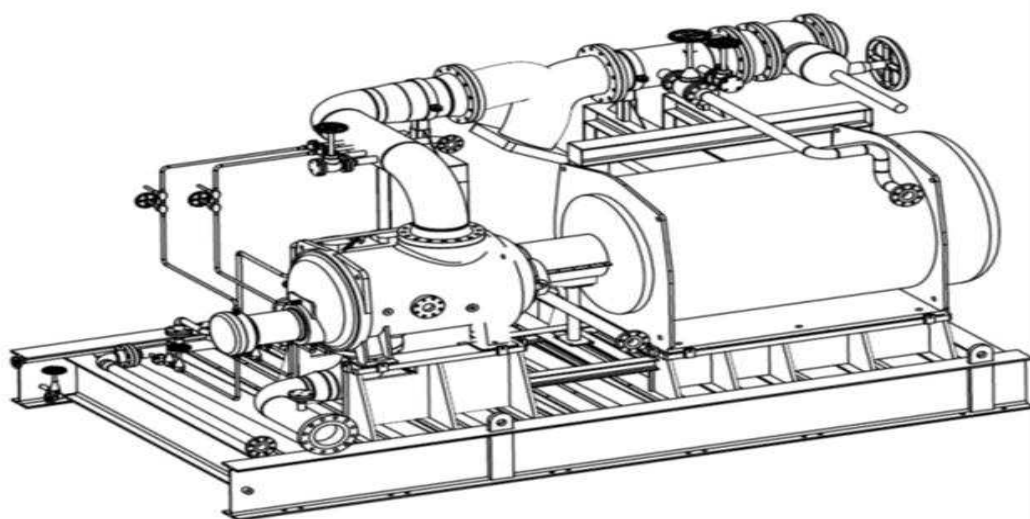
Компрессор второй ступени К-2660-1,2,3.
